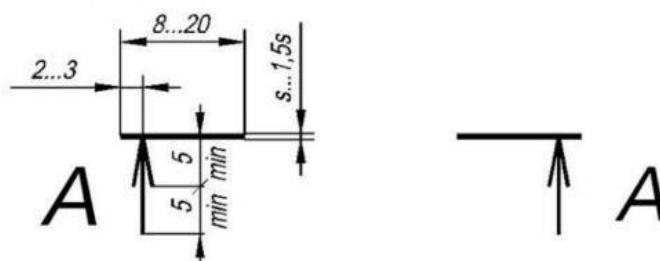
Образец изображения элементов для обозначения простых разрезов, сечений и их размеры
